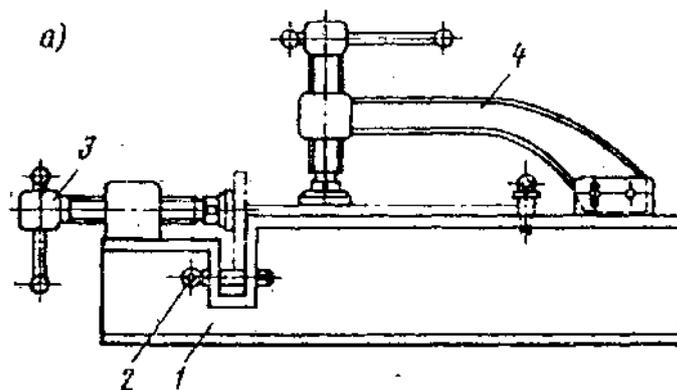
Схема устройства простейшего винтового кондуктора Источник (8)
